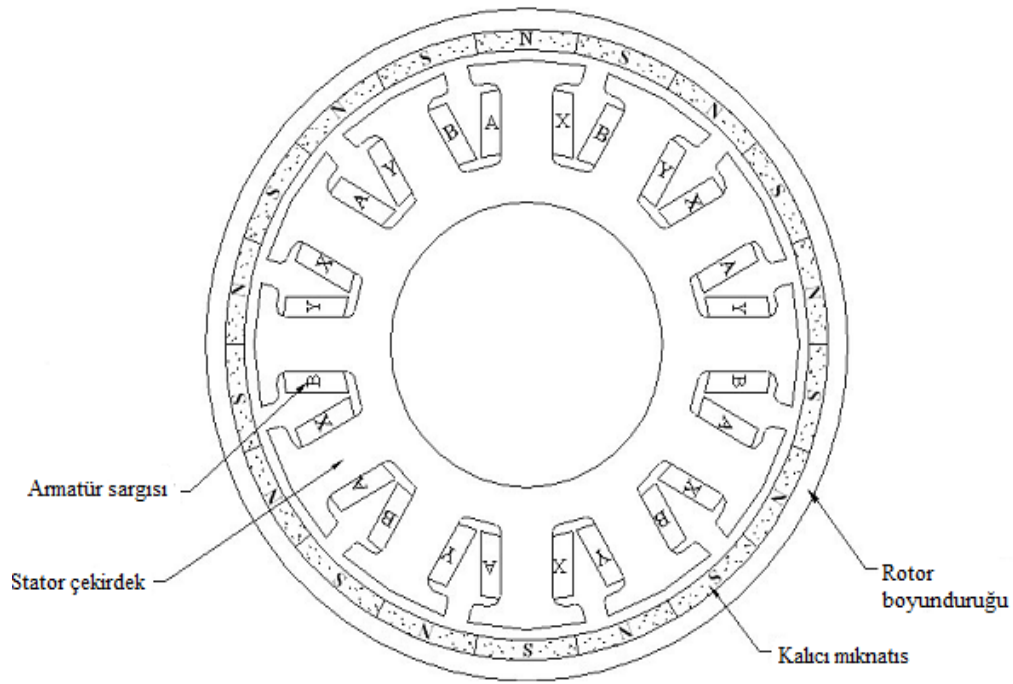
' de spindle motorun temel yapısı ve üzerinde bulunan kısımları açık bir şekilde gösterilmiştir. Genellikle spindle motorların armatür sargıları üç fazlı yapıya sahip olup, dış rotor ve yüzeyi ise kalıcı mıknatıstan oluşmaktadır. Bu spindle motorların türleri arasında; sinüzoidal dalgaya yakın EMF (Electromotive Force), küçük indüktans ve zayıf endüvi reaksiyonu şeklinde söylenebilir. Genel olarak spindle motorlar hem hızlı dinamik yanıt hem de yüksek verimlilik ve aynı zamanda istikrarlı bir hız aralığına sahiptirler. Spindle motorlar genellikle sensörsüz BLDC (Brushless Direct Current) modunda sürülürler [38].
